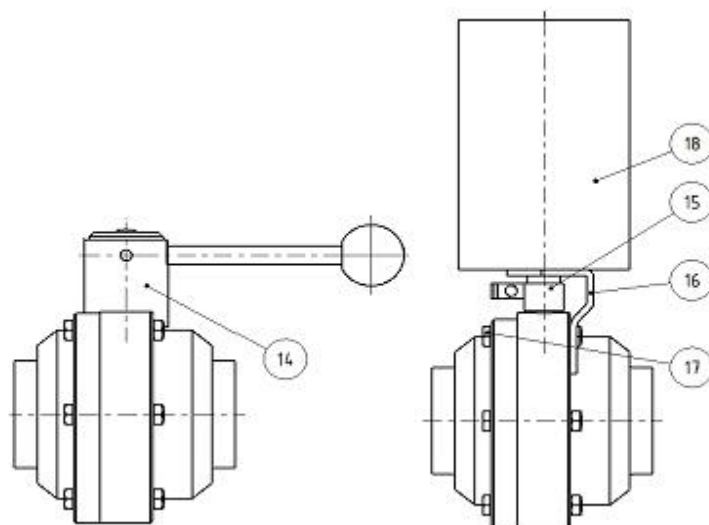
Kugelventil-SS mit Handbetätigung oder pneumatischem Antrieb
